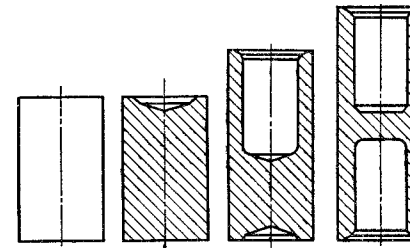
Схема последовательного выдавливания полостей с кантовкой заготовки
